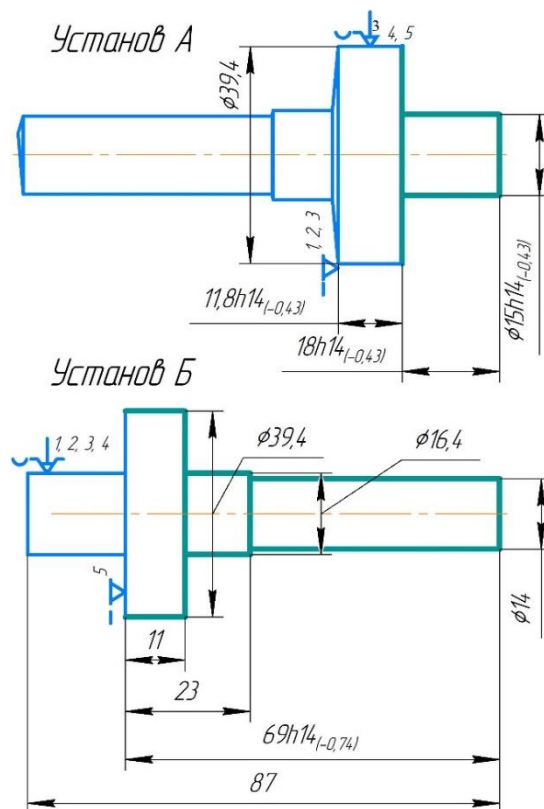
Базування заготовки на операції 015 по схемі №1
